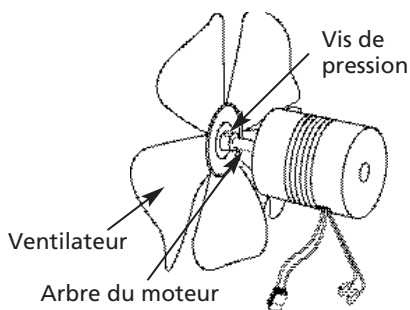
Arbre moteur du ventilateur et emplacement de la vis de pression
